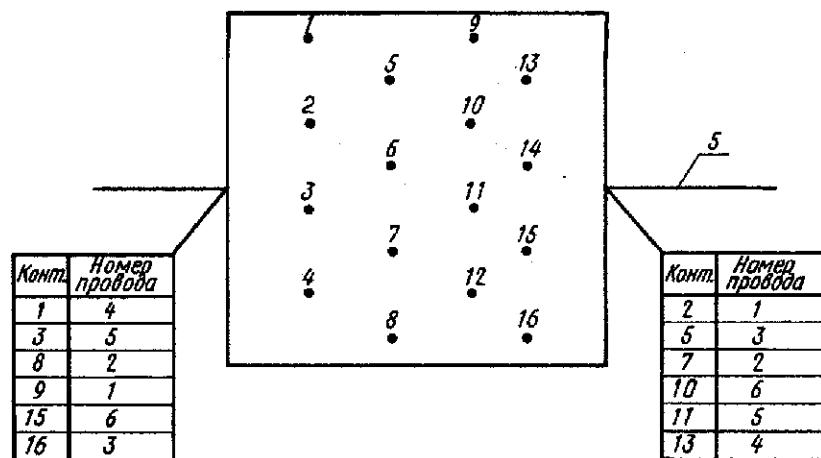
Схема присоединения проводов или жил кабеля
